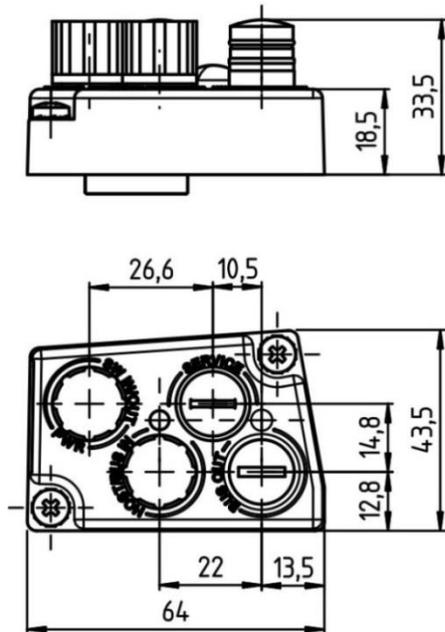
Maßzeichnung Anschlusshaube BE 901 MS SSI (alle Maße in mm)
